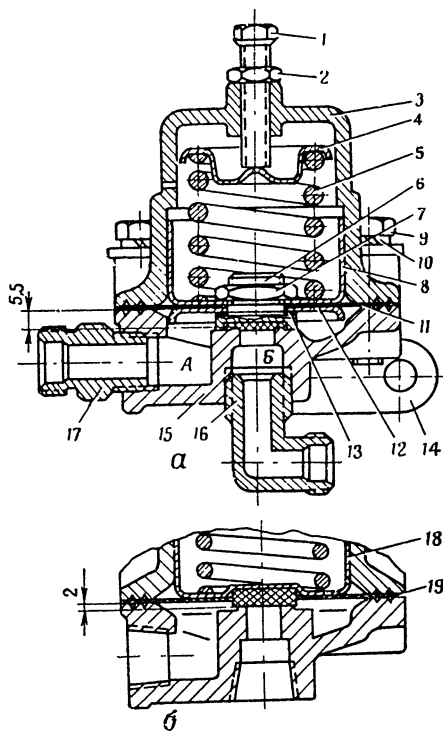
Конструктивная схема клапана-ограничителя падения давления
